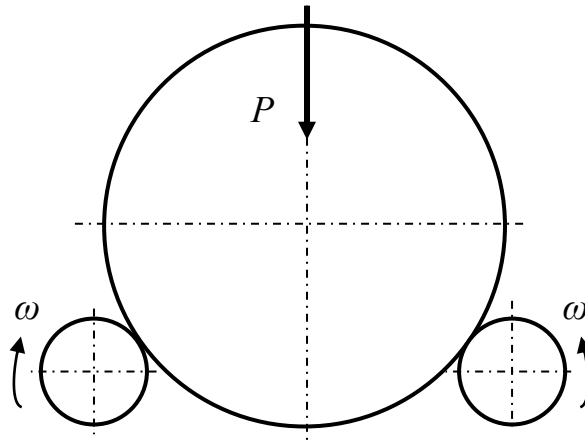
Схема базування заготовки, ω – напрям обертання валків
